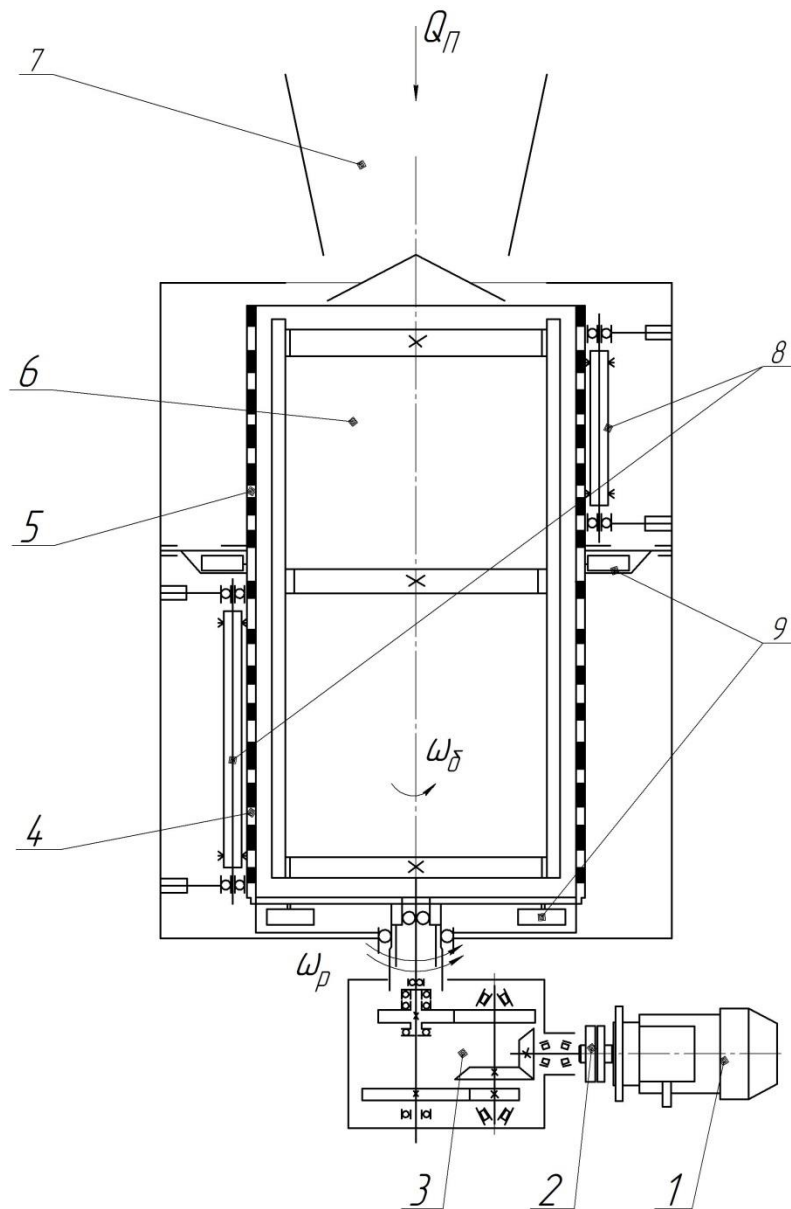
Кинематическая схема привода центробежно-решетного сепаратора
